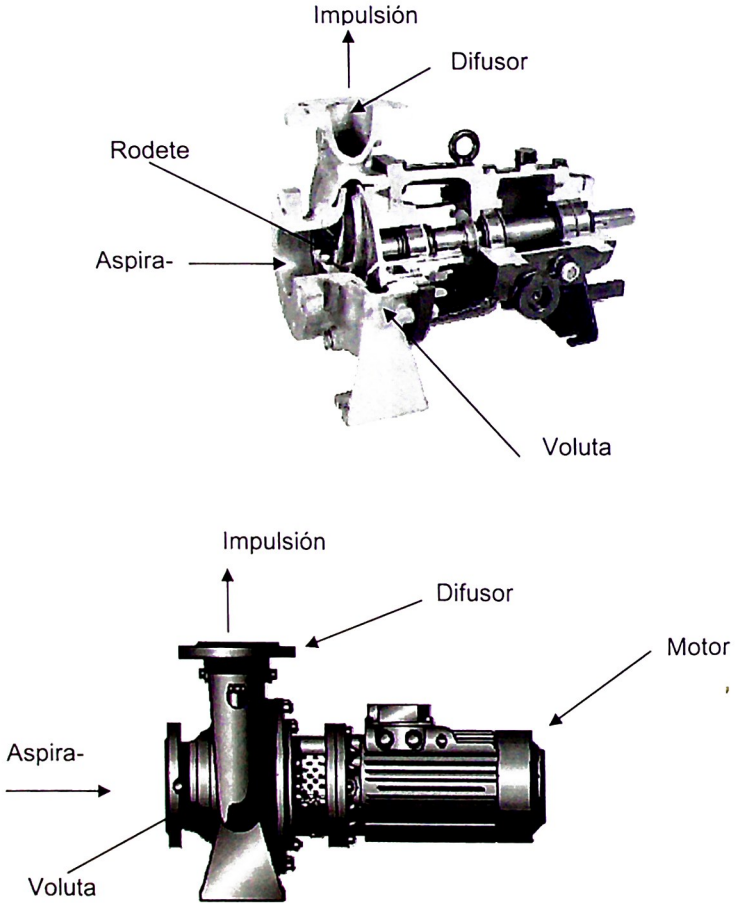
Partes de una bomba. Cortesía de Bombas Itur.
